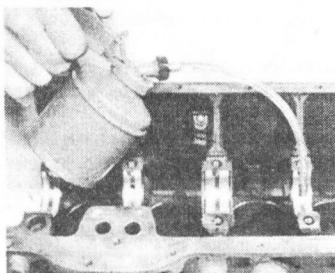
а. Обильно смажьте вкладыши коренных подшипников...
